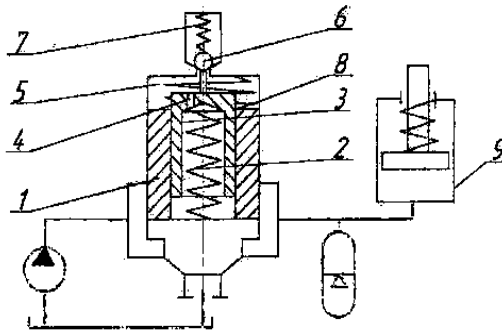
Схема гідравлічного вібраційного привода з клапаном-пульсатором: 1 - клапан другого каскаду 2 - пружина; 3 - штовхач; 4 - отвір дросельний; 5 - порожнина надклапанна; 6 - кулька; 7 - пружина; 8 - пружина; 9 - порожнина циліндра
